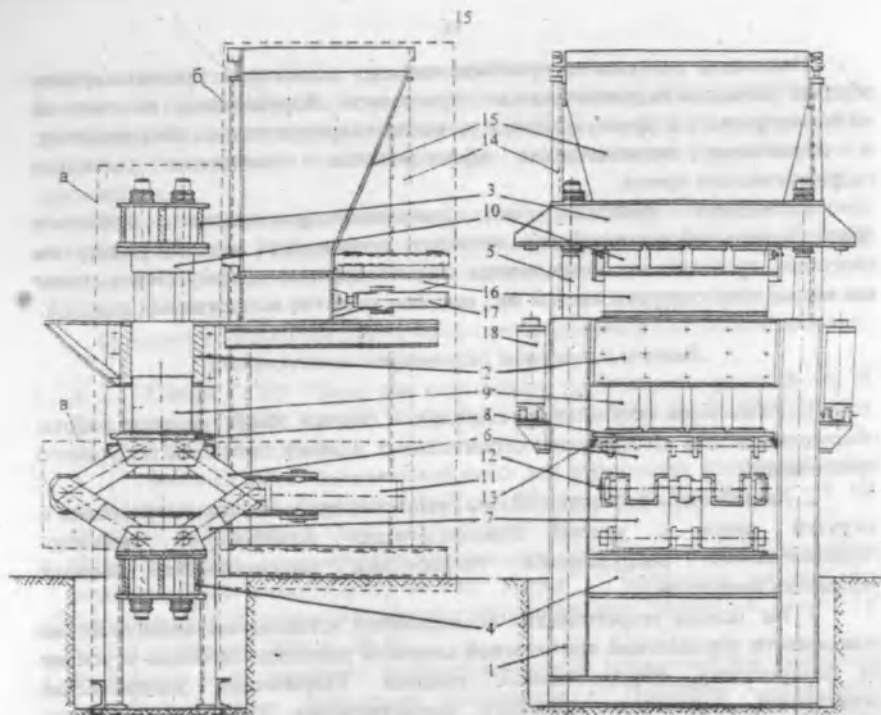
Конструкция рычажно-гидравлического оборудования: а) прессующая часть, б) загрузочный механизм, в) механизм прессования прессового оборудования; 1 — рама; 2 — матрица; 3, 4 — верхняя и нижняя траверсы; 5 — направляющая тяга; 6, 7 — верхняя и нижняя пара рычагов; 8 — промежуточная балка; 9, 10 — нижние и верхние пуансоны; 11 — прессующий гидроцилиндр; 12 — тяга; 13 — упор; 14 — рама бункера; 15 — бункер; 16 — питатель с отсекателем; 17 — гидроцилиндр питателя; 18 — гидроцилиндр выпрессовки
